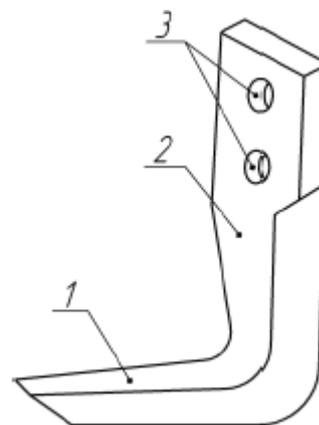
L-образный наружу отогнутый нож: 1 – подрезающее лезвие; 2 – стойка; 3 – отверстия для крепления к ротору
